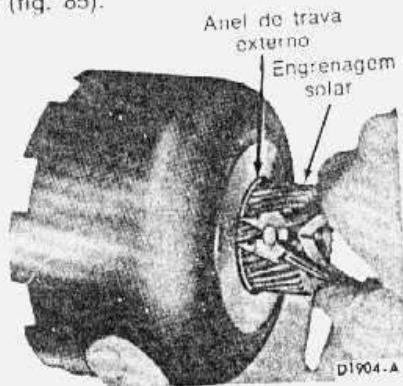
remoção ou instalação do anel de trava da engrenagem solar
